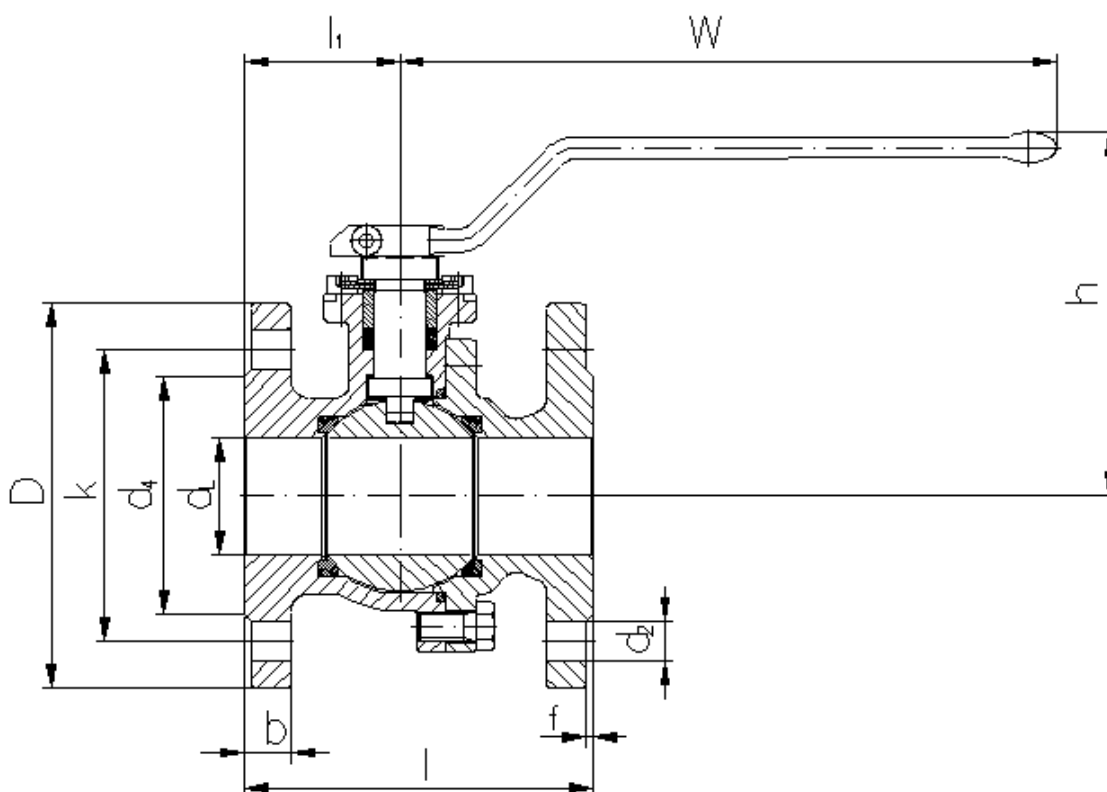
Kugelhahn mit Flanschanschluss nach DIN EN 1092-1 Form B1; Baulänge Grundreihe 27 (kurz) nach EN 558-1 (F18 nach DIN 3202 Teil 1)
